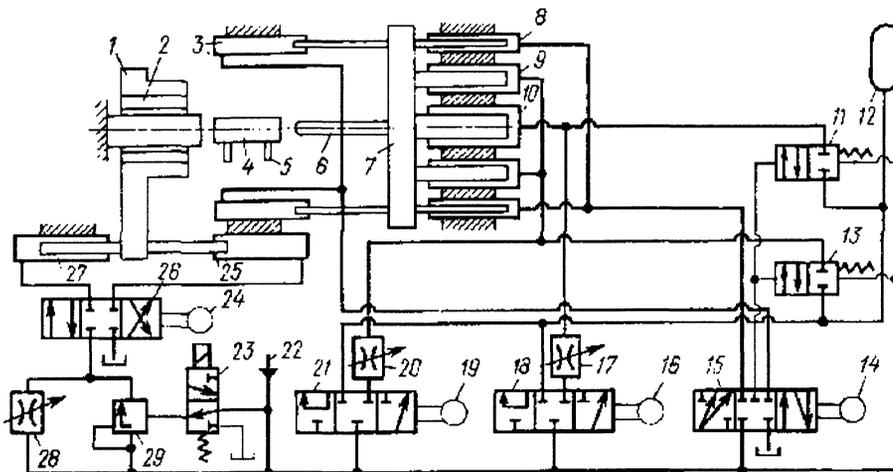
Принципиальная гидромеханическая схема прессы для прошивки заготовок
